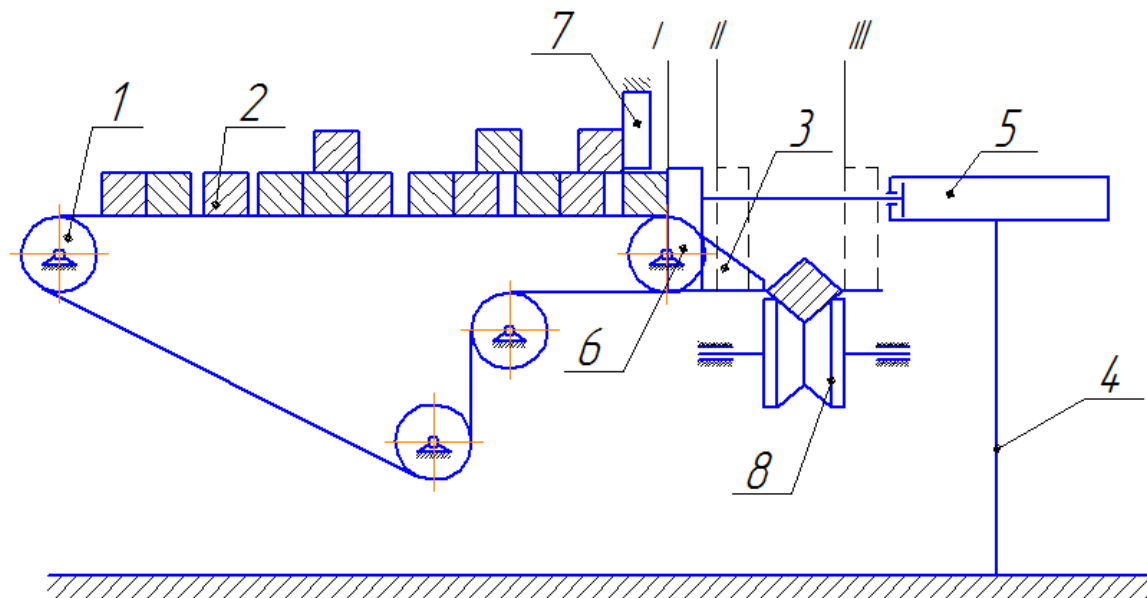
Автоматическое устройство для поштучной подачи проката в зону обработки
